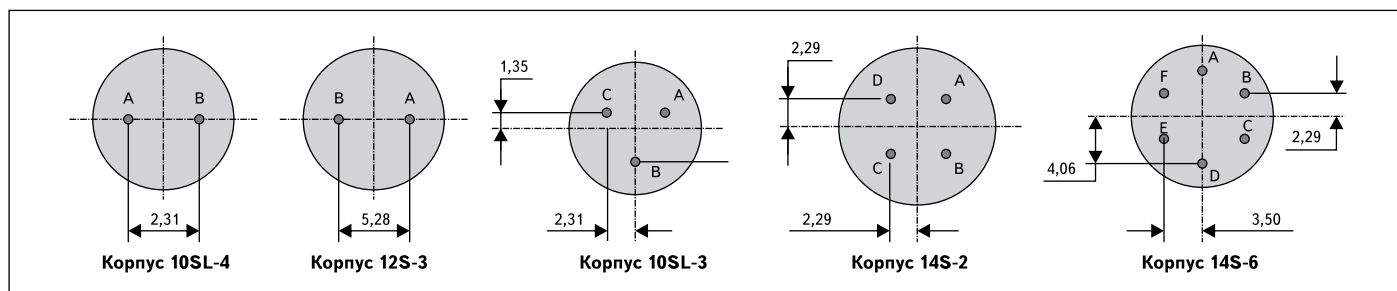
Расположение контактов в корпусах разъемов по стандарту MIL-DTL-5015
